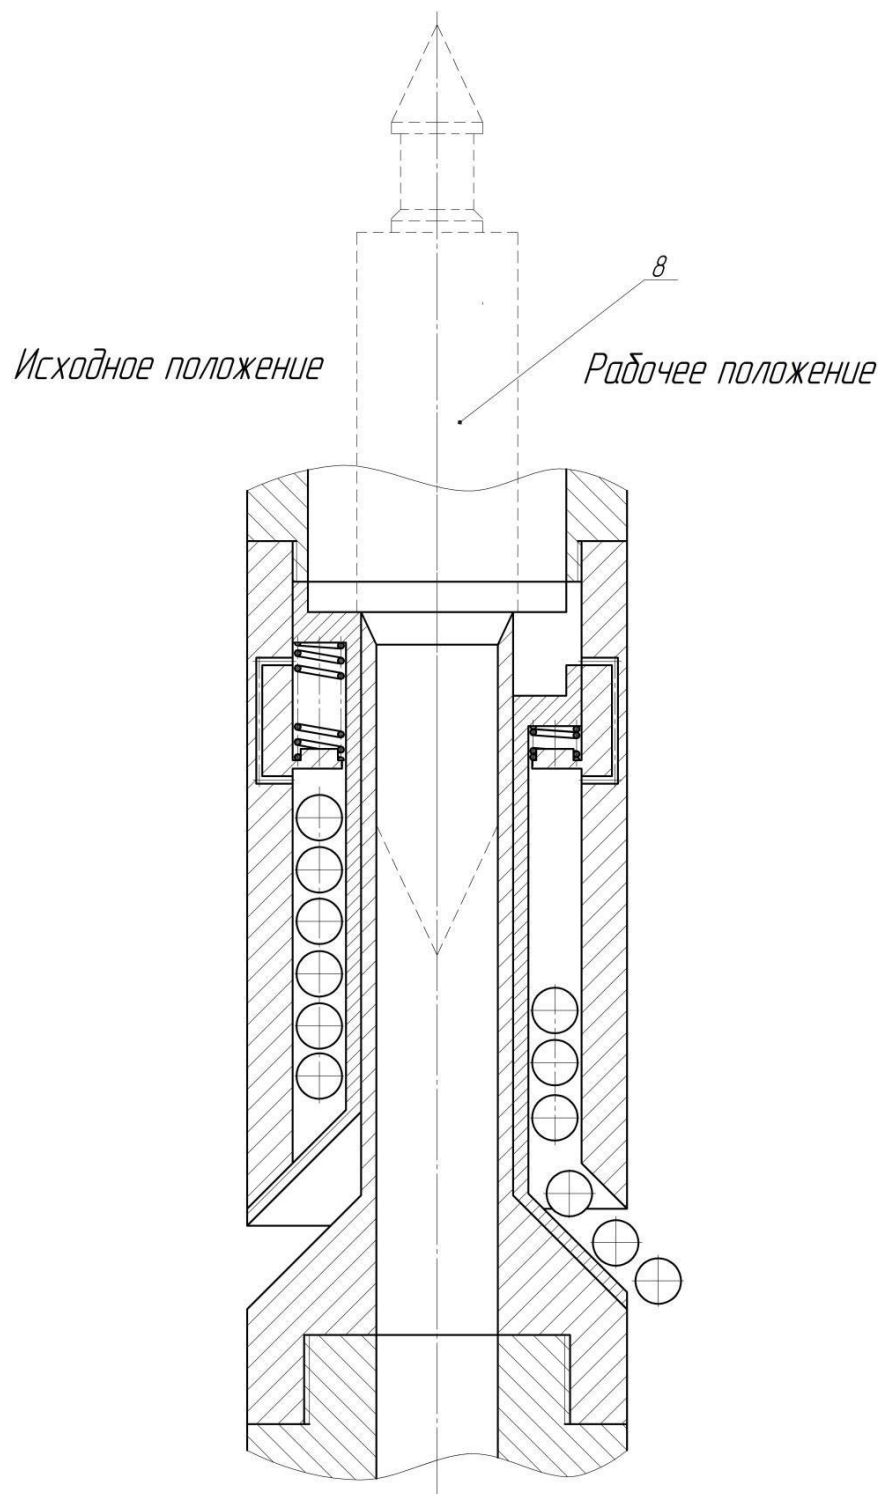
Комбинированный разрез забойного шаропитателя I:
